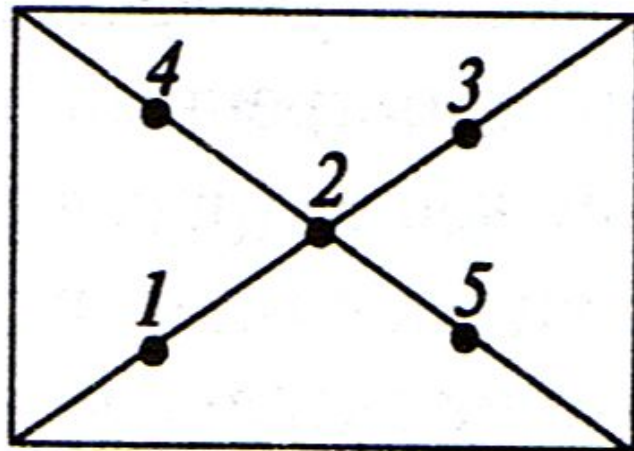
Отбор средней пробы металла или сплава высверливанием
